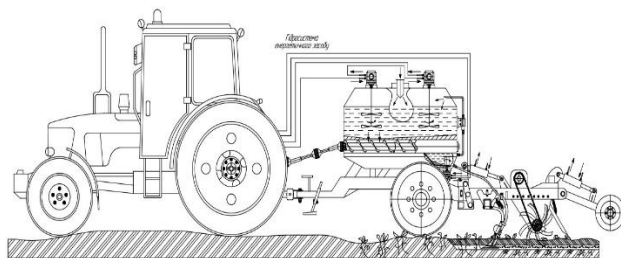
Загальний вигляд машинно-тракторного агрегату для технології Strip-till
